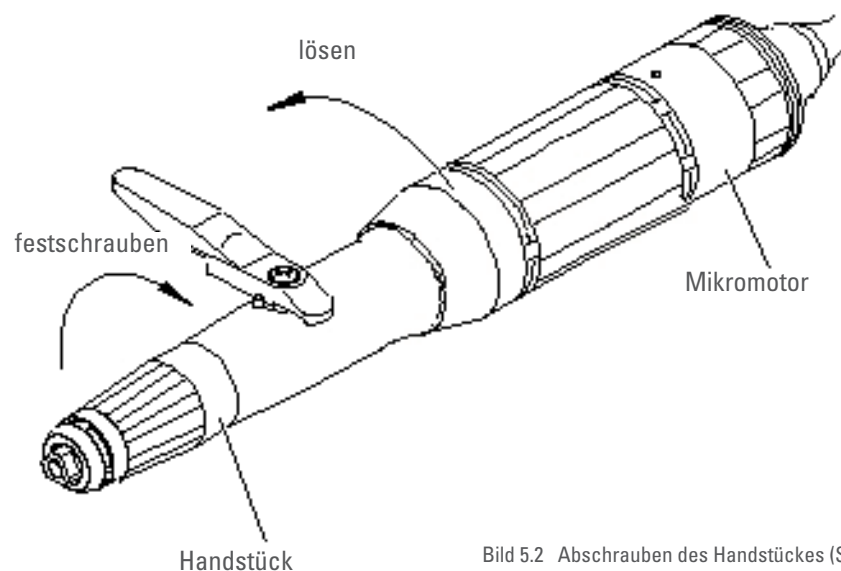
Abschrauben des Handstückes (Symbolzeichnung)
